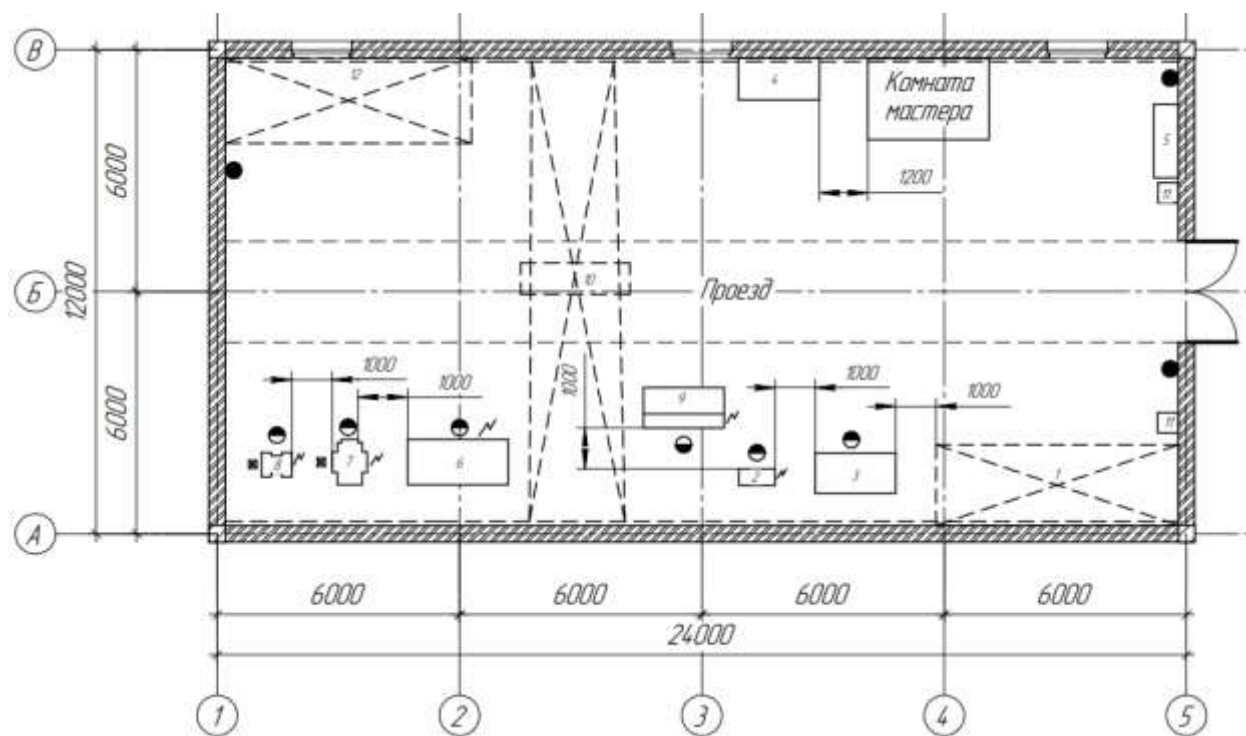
Планировка участка сборки и сварки пескоструйной камеры
